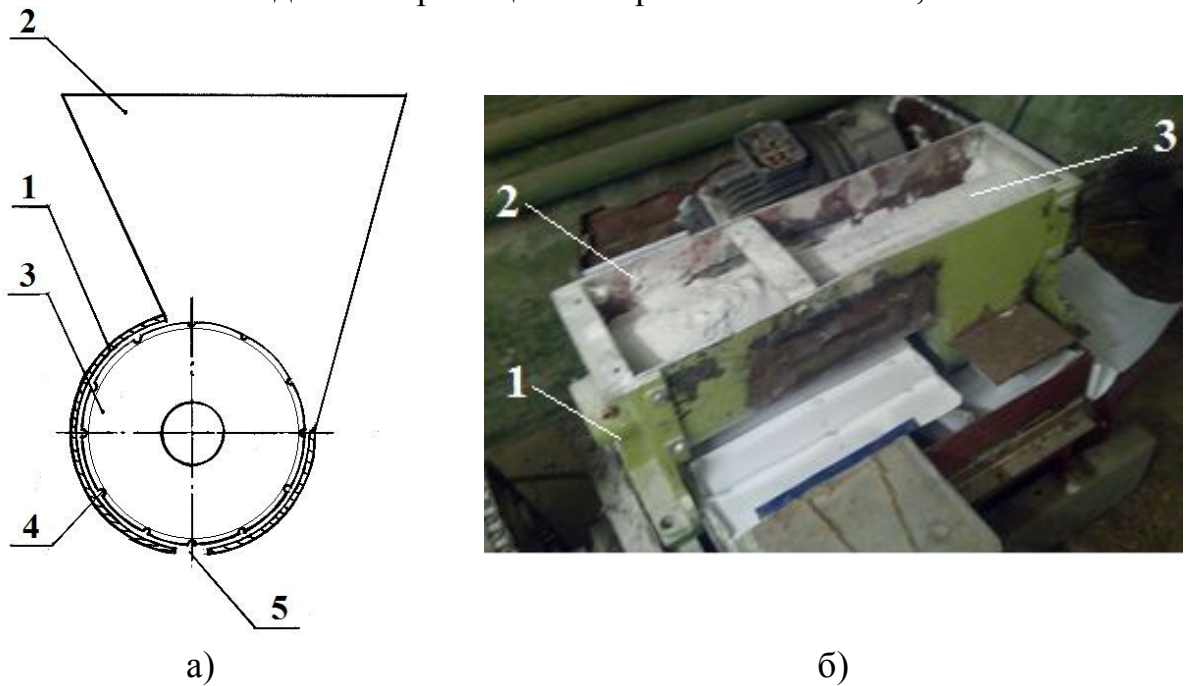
Дозатор для внесення пиловидного консерванту в силосну масу: а) конструктивно-технологічна схема; б) загальний вигляд; 1 – корпус; 2 – завантажувальний бункер; 3 – барабан; 4 – комірка напівсферичної форми; 5 – вивантажувальна щілина
